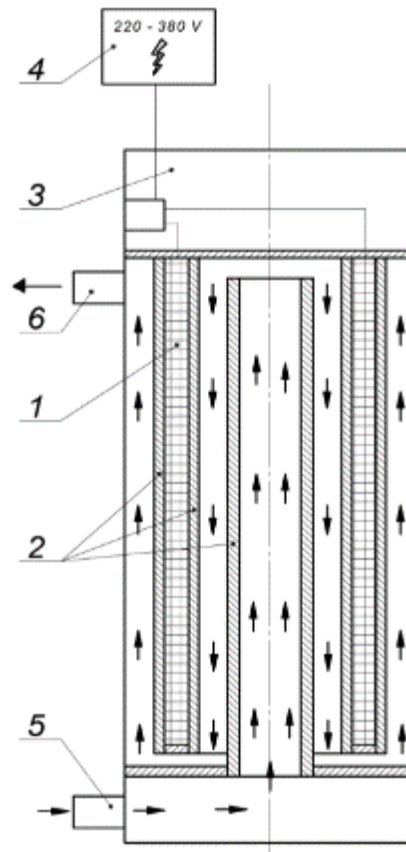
Вихровий індукційний нагрівач: 1 – котушка; 2 – теплообмінник; 3 – клемна коробка; 4 - шафа управління; 5 – вхідний патрубок; 6 - вихідний патрубок
